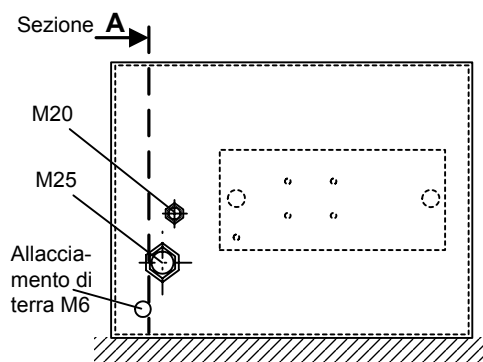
Disegno di montaggio resistenza di frenatura
